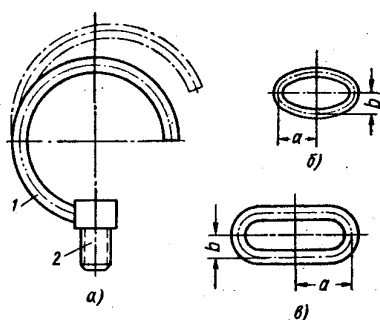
Приборы с одновитковой трубчатой пружиной:
